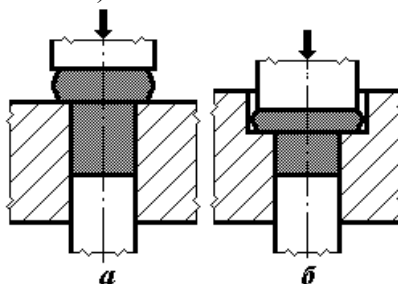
Схемы высадки: а – открытой; б – закрытой.
